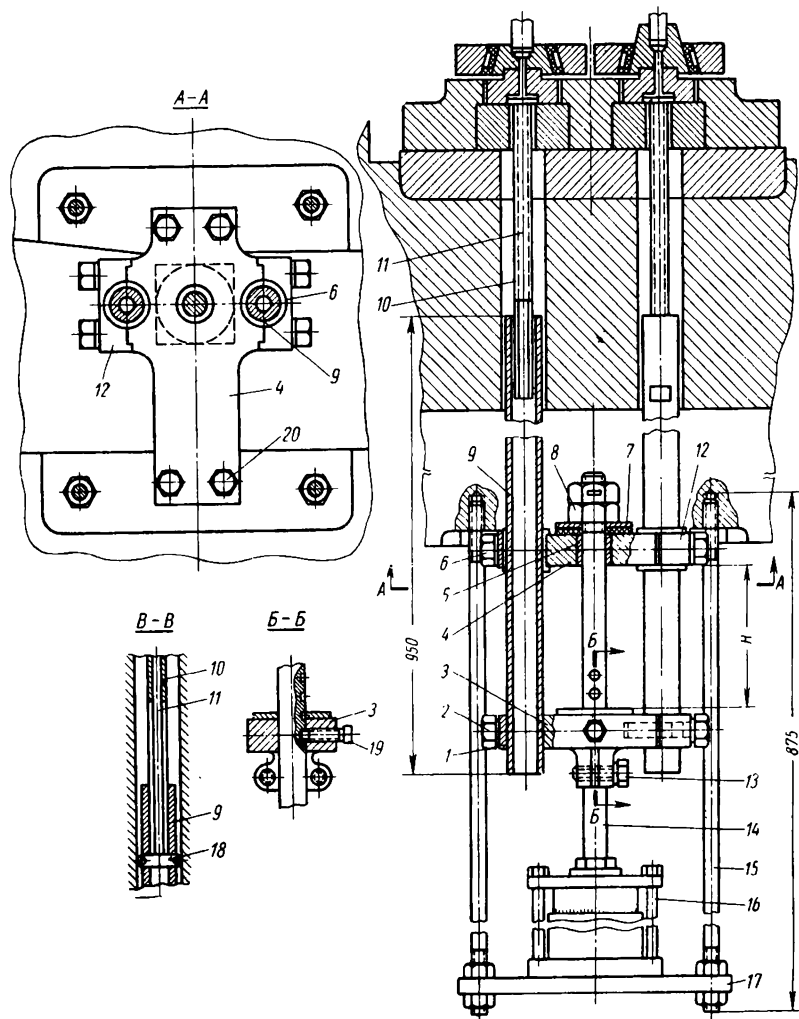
Пневматический выталкиватель: 1 — зажим нижний; 2, 6, 13 и 20 — болты; 3 — подвижная траверса; 4 — неподвижная траверса; 5 — втулка; 7 — шайба; 8 — гайка; 9 — трубка; 10 — направляющая втулка шпильки; 11 — выталкивающая шпилька; 12 — верхний зажим; 14 — шток; 15 — тяга; 16 — тяга воздушного цилиндра; 17 — опора воздушного цилиндра; 18 — чека; 19 — фиксационный болт
